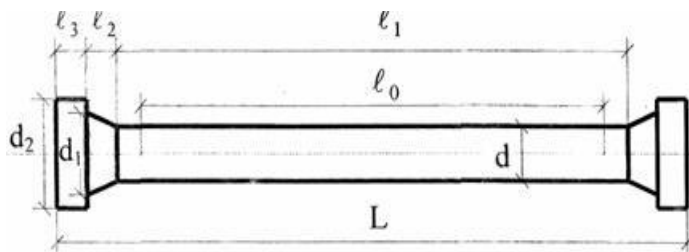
Цилиндрический образец для испытания на растяжение
